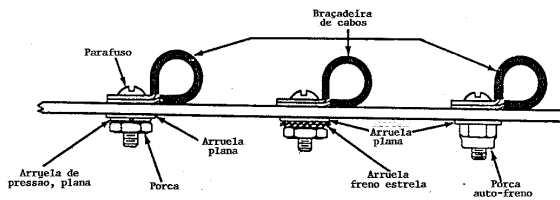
Ferragens típicas de montagem para braçadeiras de cabo.
